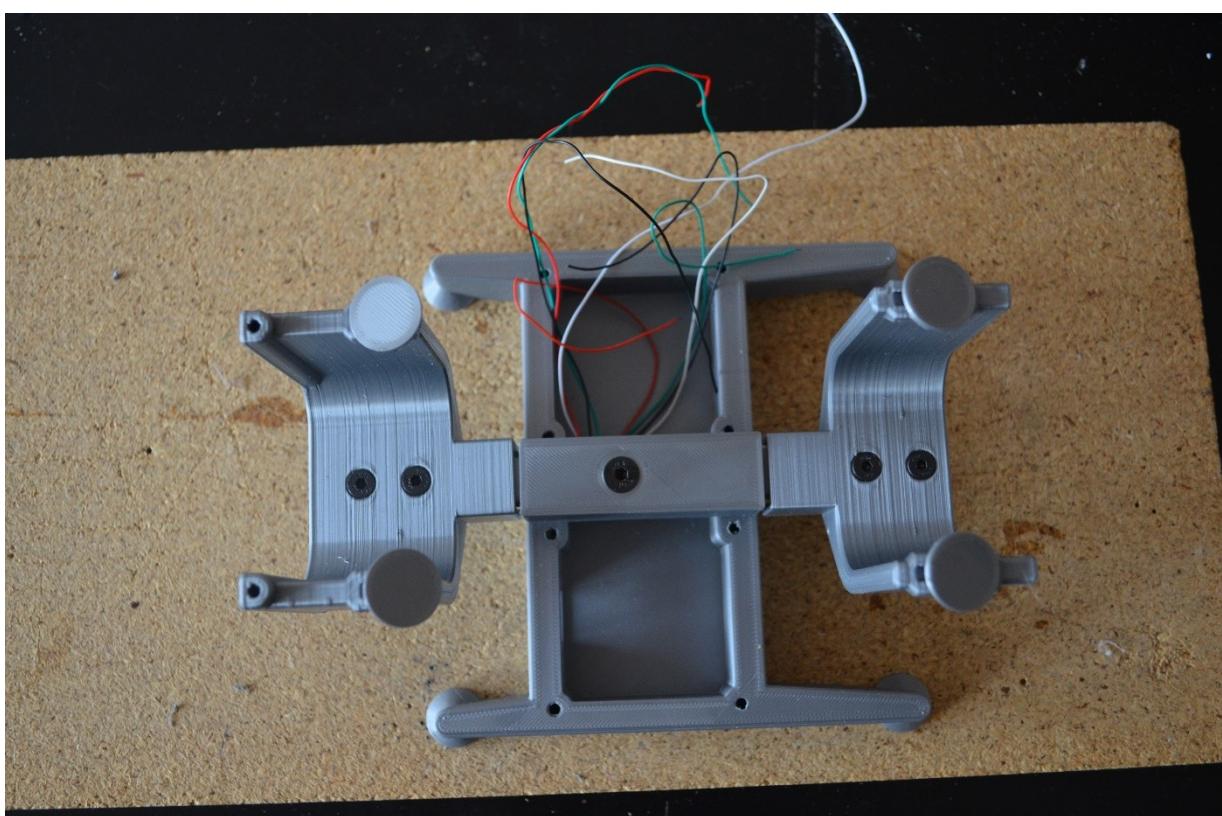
Etape 3 – supports avant & arrière de planeur installés.
